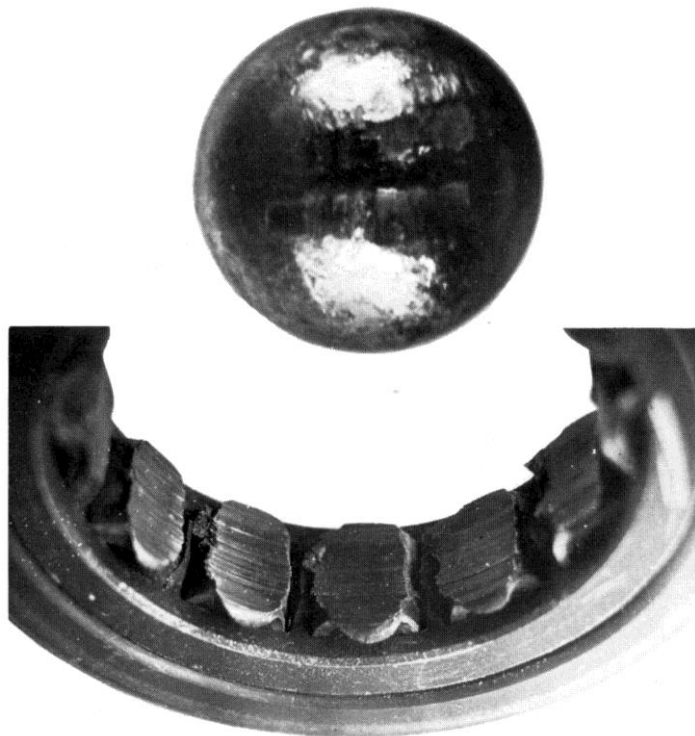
fundición y arrastre de los elementos rodantes [3].
